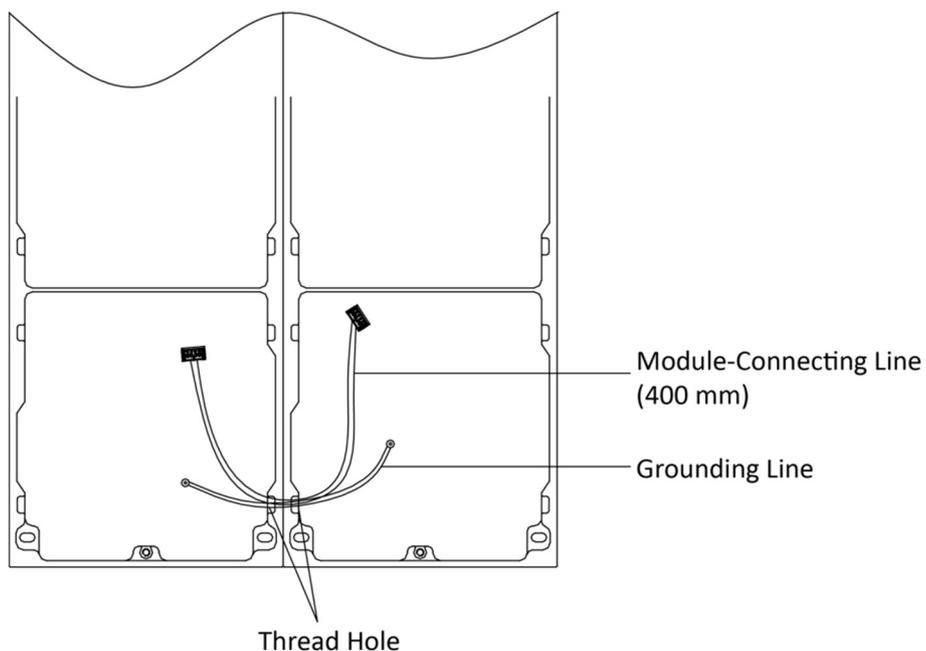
Posizionamento del cavo di messa a terra e del cavo di collegamento al modulo
